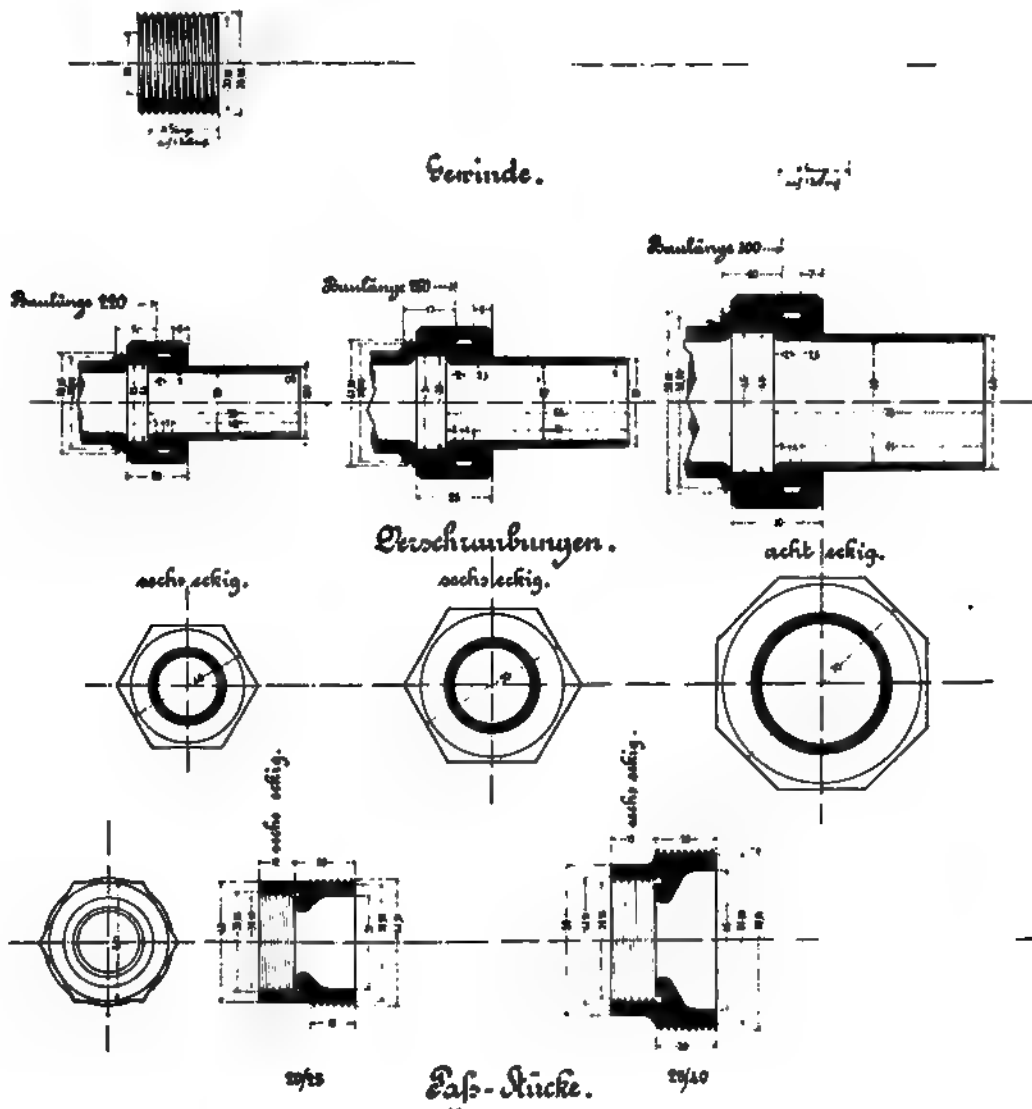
Gewinde, Verschraubungen und Paßstücke zu Wassermessern.
